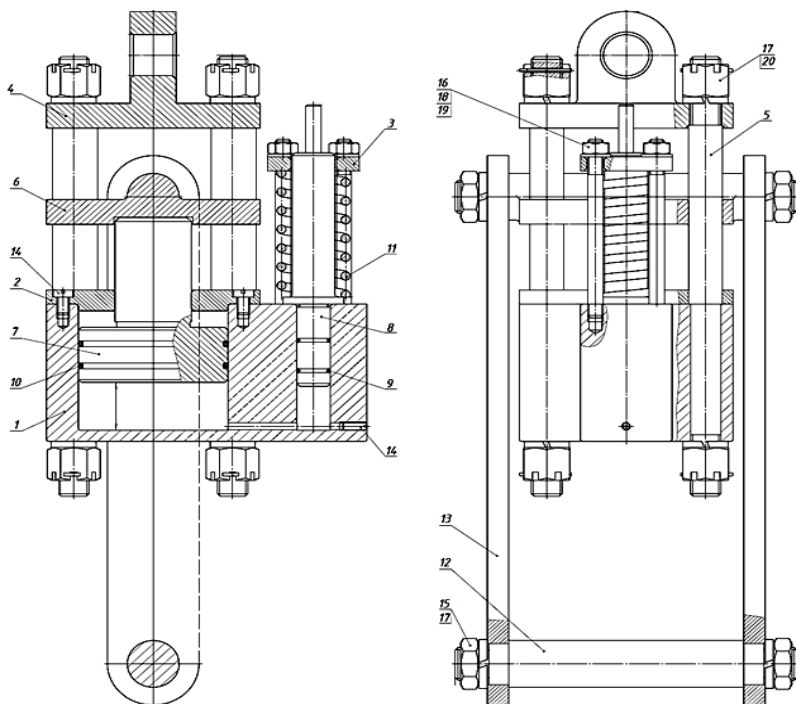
Конструкция активного демпфера [7]: 1 – корпус; 2 – крышка корпуса; 3 – крышка; 4 – фланец; 5 – стойка; 6 – траверса; 7 – поршень; 8 – толкатель; 9, 10 – кольцо уплотнительное; 11 – пружина; 12 – ось блока; 13 – серьга
